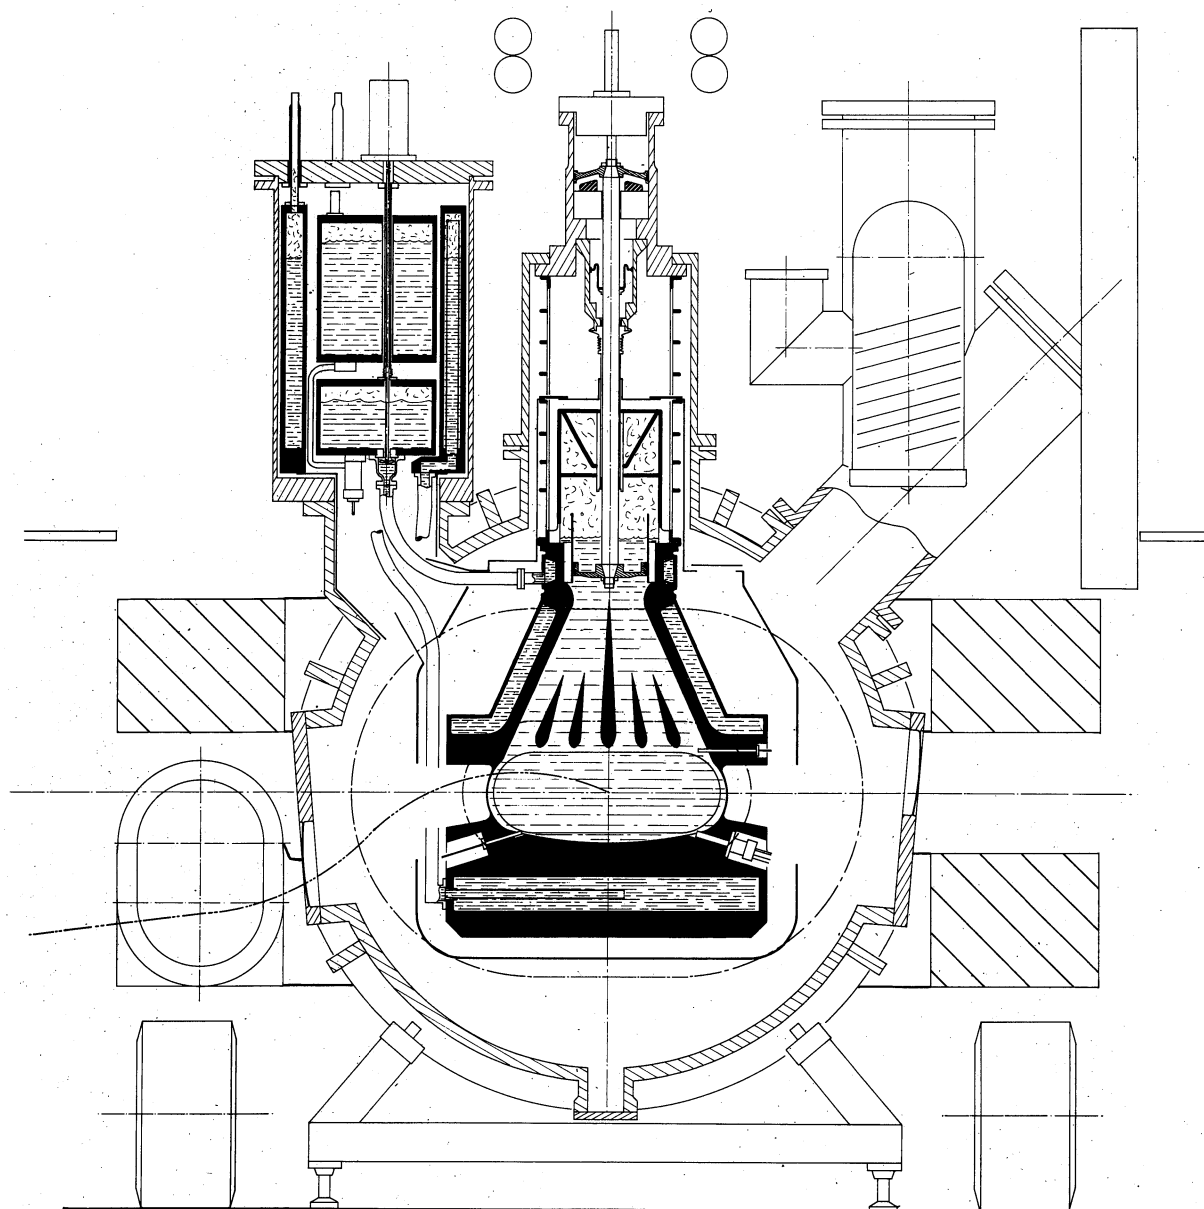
Plan coupé de la C.B.H. 81 parallèlement au plan de référence
